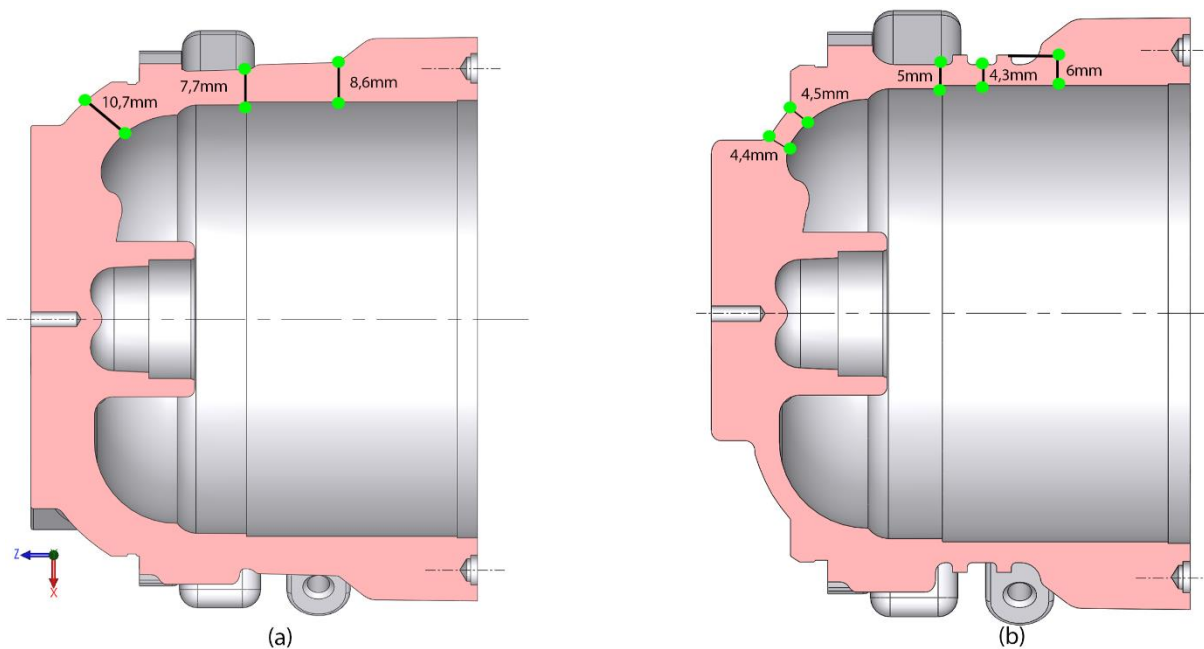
a) Vista em corte do componente original e b) vista em corte da nova configuração com espessura de parede reduzida.
